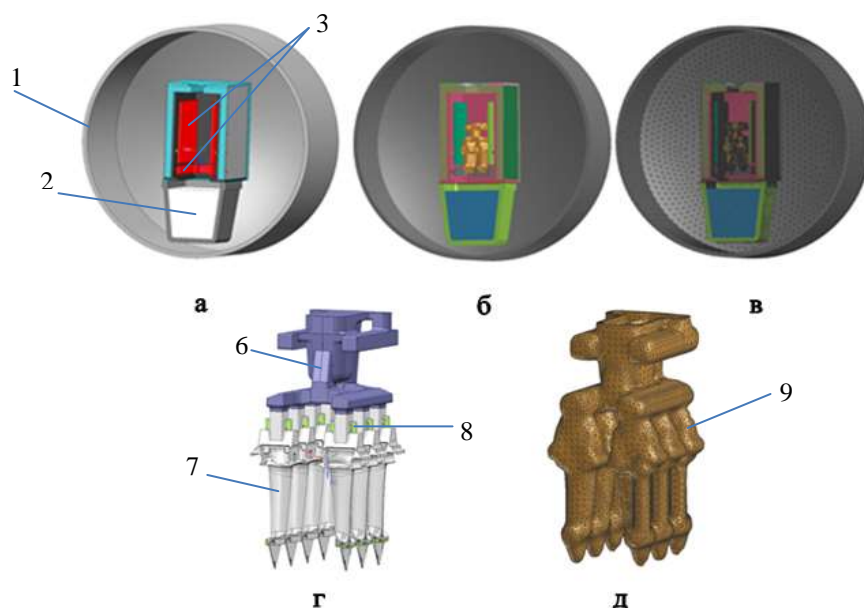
CAD-модель УППФ (а) и литейного блока (г) в сборе (б), КЭМ литейного блока (д) и УППФ (в) в сборе: 1 – обечайка; 2 – алюминий; 3 – нагревательный элемент; 4 – корпус; 5 – ванна; 6 – литниково-питающая система; 7 – лопатка; 8 – керамический стержень; 9 – керамическая оболочковая форма
